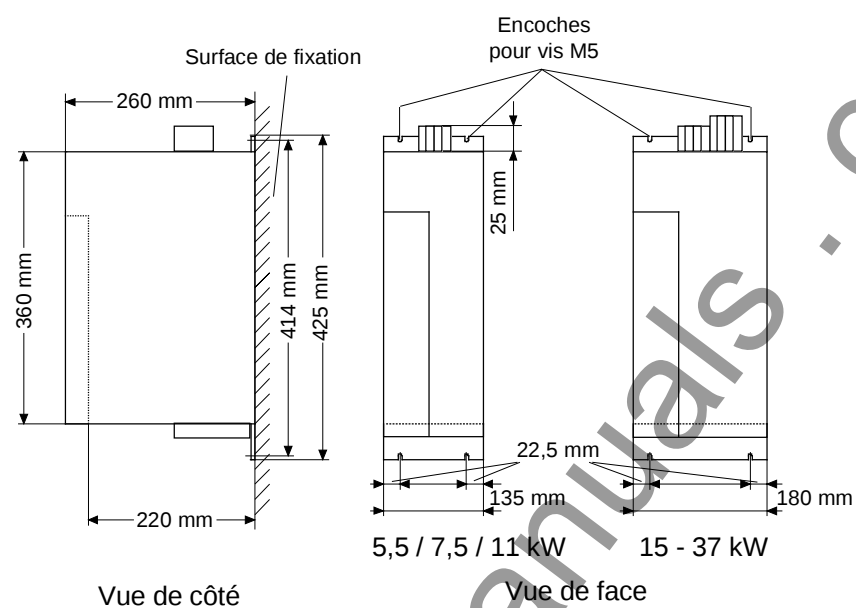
Encombrement, boîtiers de largeur 135 mm et 180 mm
